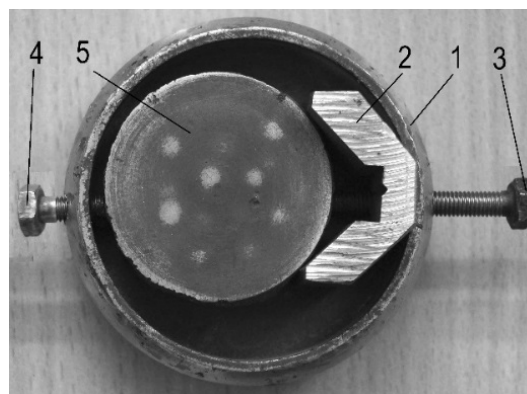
Узел крепления образца: 1-опора; 2-призма; 3-регулируемый винт призмы; 4-зажимной винт; 5-образец
